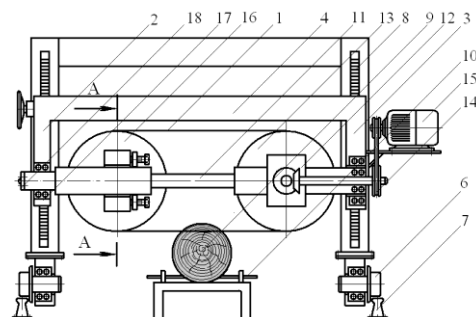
Общий вид ленточнопильного станка (вид спереди):
